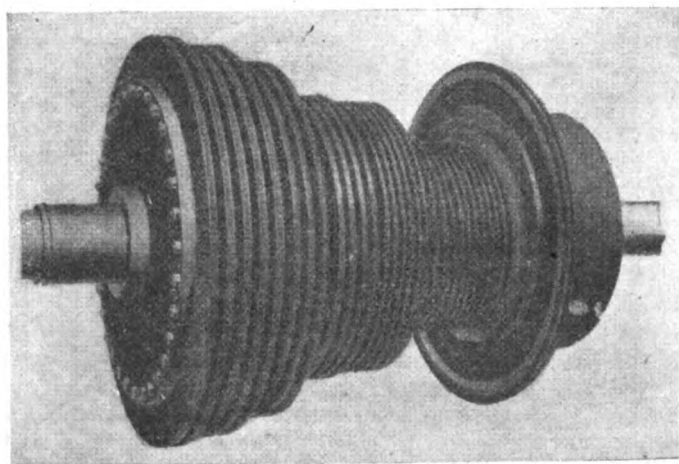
Rotore con tamburo a impulso di una turbina Belliss e Morcom.
